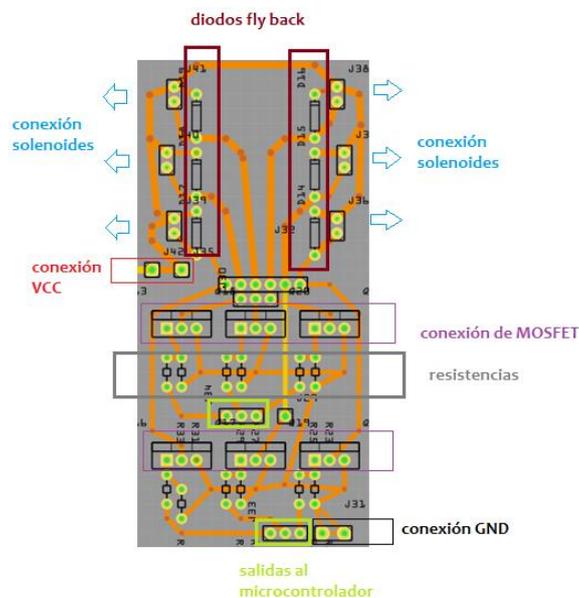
Distribución de componentes en el PCB del módulo de lectura
